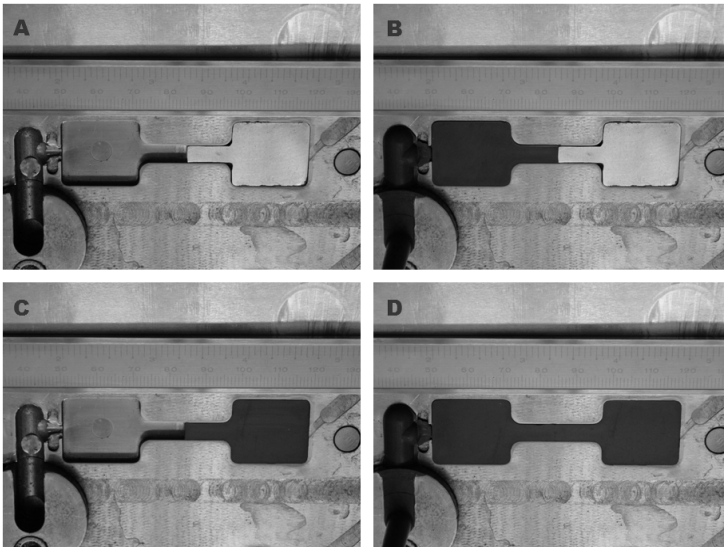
Etapas da Sobreinjeção. Passo A: Inserto fechando meia cavidade. Passo B: Injeção feedstock 1. Passo C: Remoção do inserto e posicionamento material 1. Passo D: Injeção do feedstock 2.
